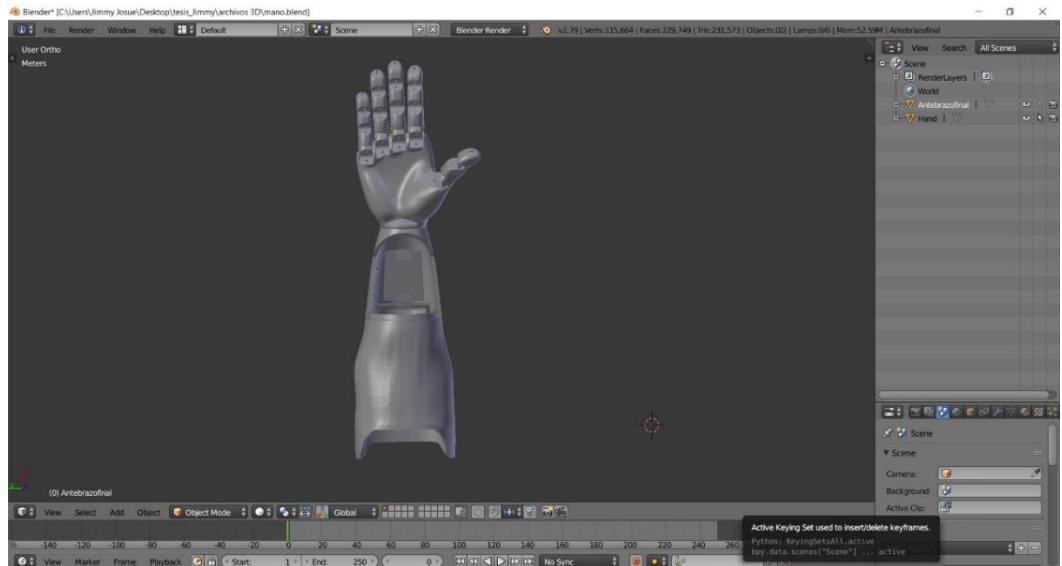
Vista frontal de la Prótesis Completa en Blender.
